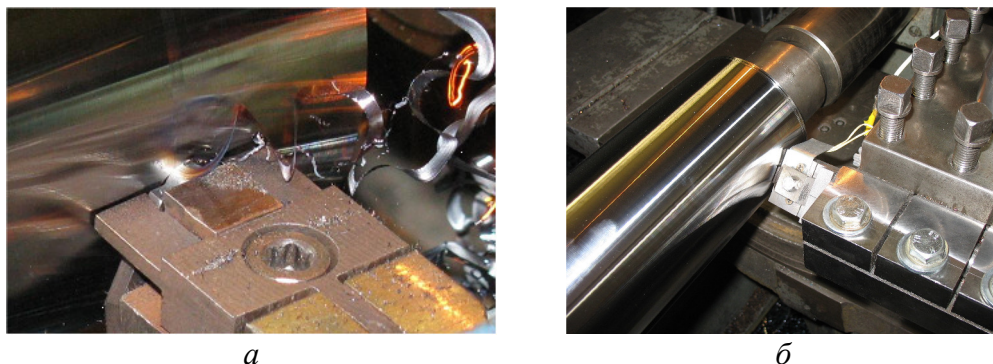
Обработка деталей из закаленной стали резцом с цилиндрической передней поверхностью (а) и «бреющим» резцом (б)
